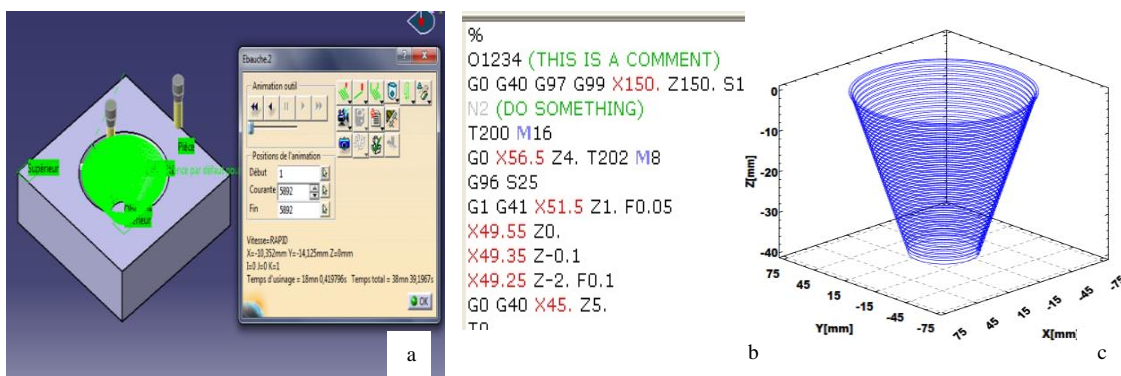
Génération de la trajectoire à implémenter sur la machine CNC à partir de la pièce
